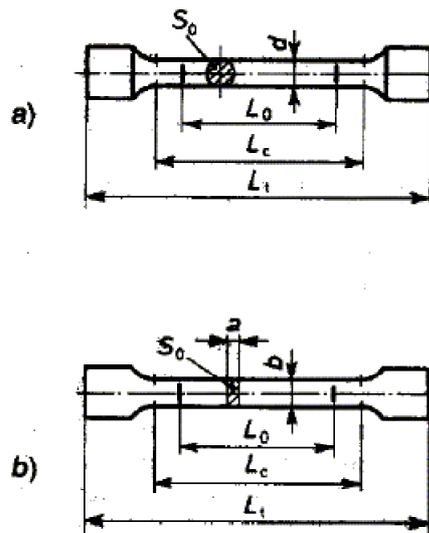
Provini per prove di trazione: a) sezione circolare; b) sezione rettangolare
